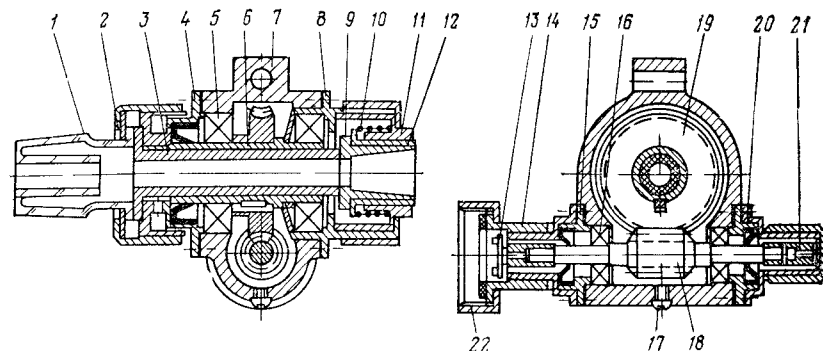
Червячный редуктор с торцевым вакуумным уплотнением
